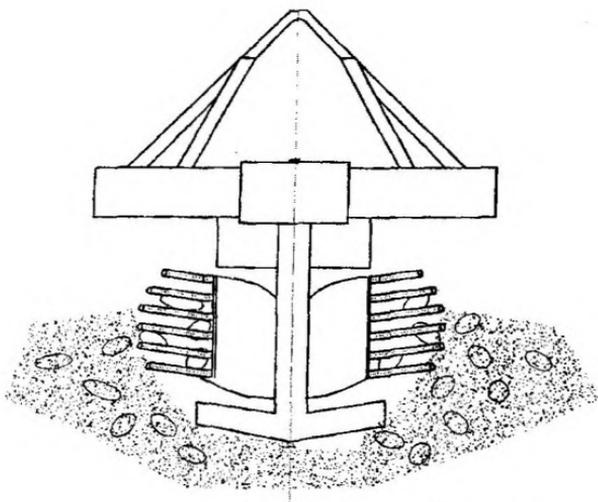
Вид сзади подкапывающего рабочего органа агрегата
